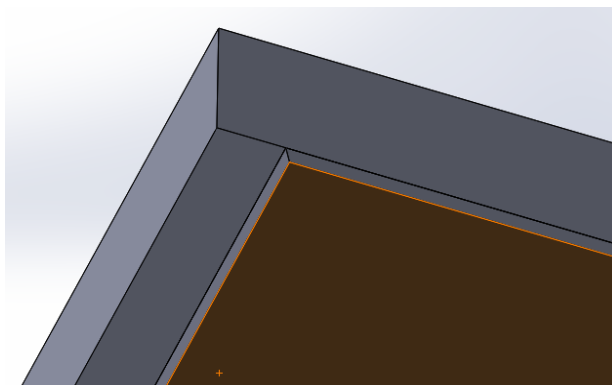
Зліпок пластини зі зварним швом на площині паралелепіпеда
